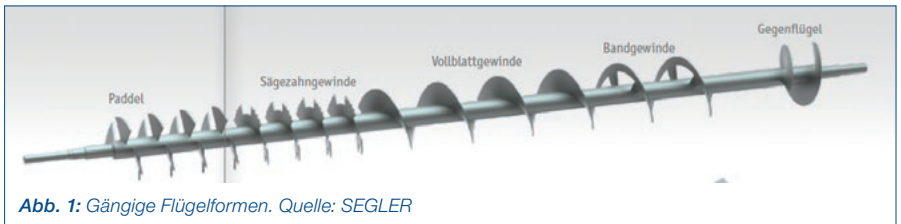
Gängige Flügelformen. Quelle: SEGLER
